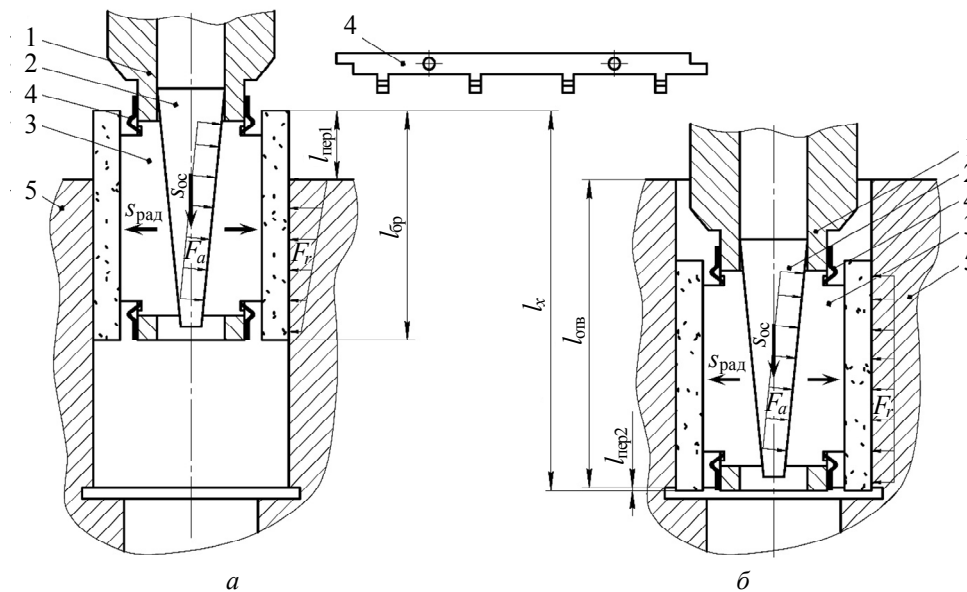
Инструмент для хонингования отверстий: 1 — корпус, 2 — игла разжима, 3 — режущие элементы, 4 — плоская лепестковая пружина, 5 — обрабатываемая деталь; F_a — эюра активных усилий, F_r — эюра реактивных усилий, $l_{\text{отв}}$ — длина хонингуемого отверстия, $l_{\text{бр}}$ — длина режущих элементов инструмента, $l_{\text{пер1}}$ и $l_{\text{пер2}}$ — перебеги режущей части инструмента соответственно с одной и с другой стороны отверстия
